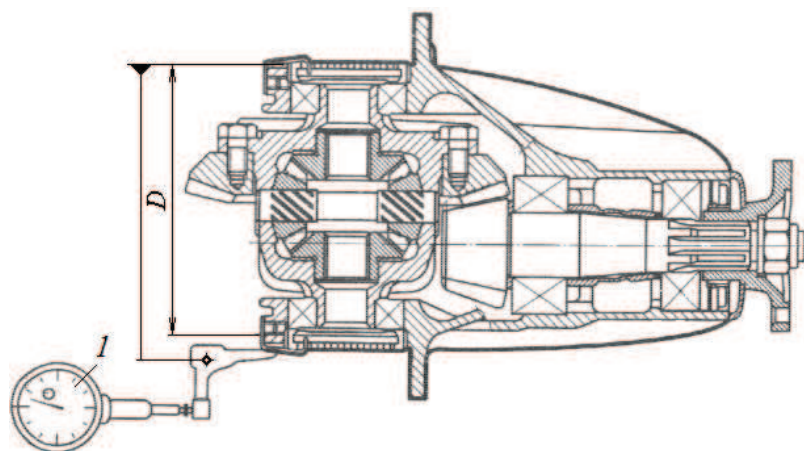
Схема регулирования осевого натяга в подшипниках дифференциала с помощью специального контрольного приспособления: 1 – индикатор часового типа; D – расстояние между верхними точками крышек подшипников
